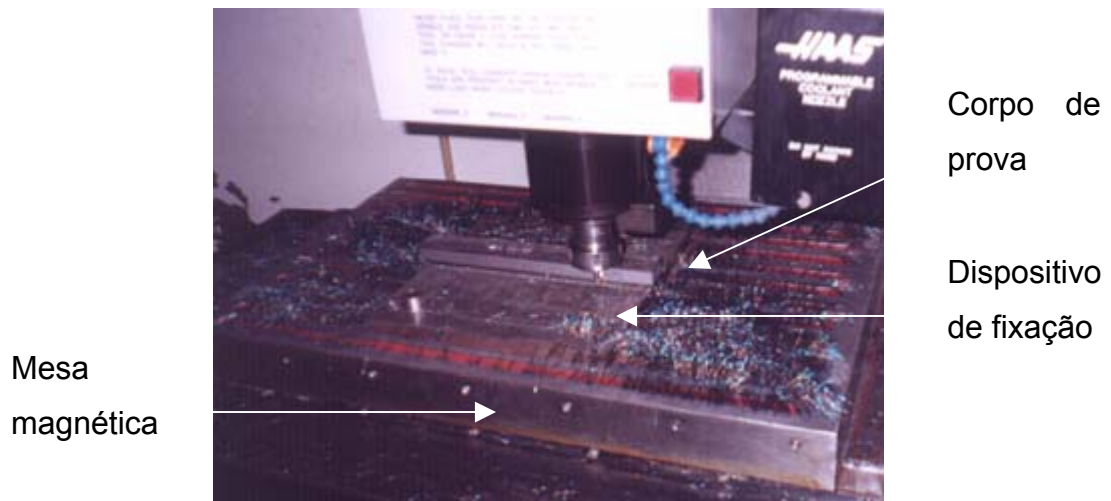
Montagem básica dos corpos de prova na máquina-ferramenta.
